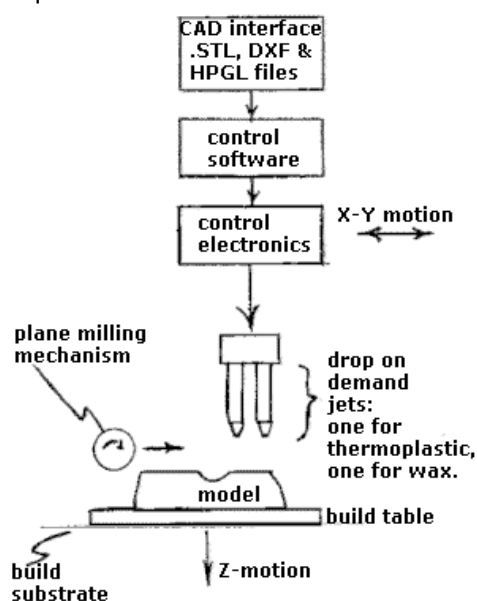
Esquema desenhado do interface Sanders ModelMaker
